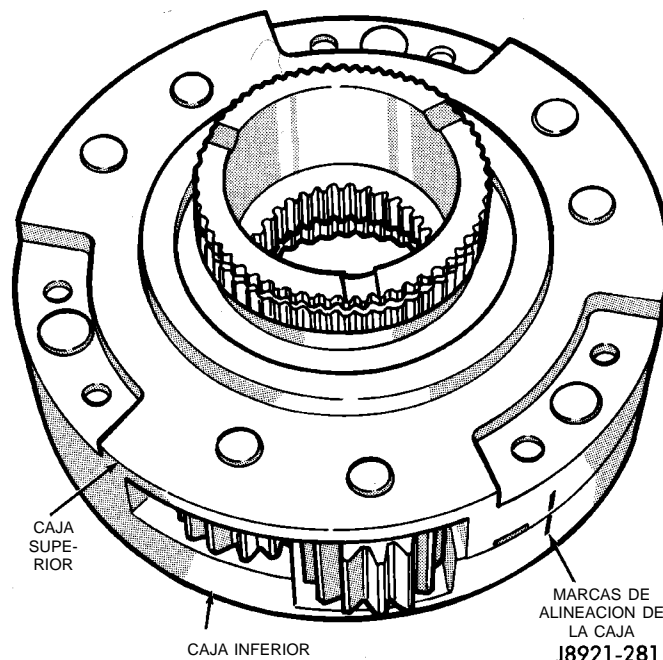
Instalación del engranaje de la rueda propulsora del diferencial
